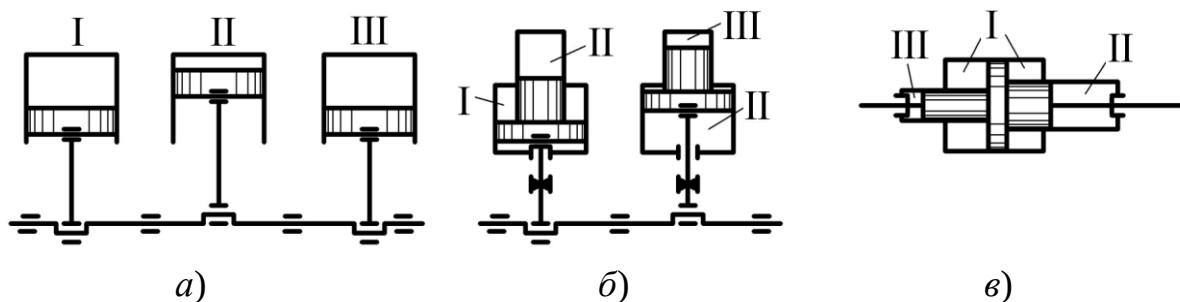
Некоторые конструктивные схемы трехступенчатых компрессоров:
